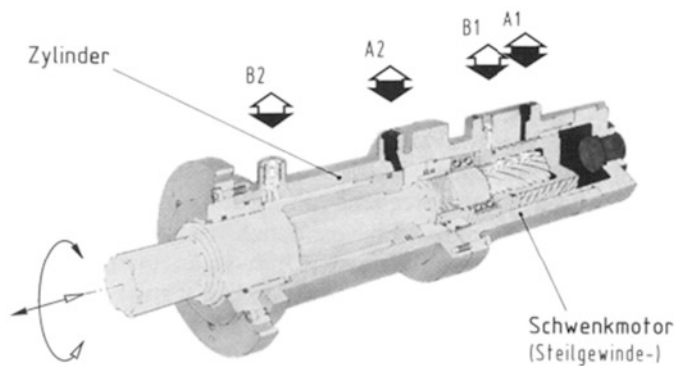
Steilgewinde-Dreh-Hubzylinder in der Gestaltungsvariante Zylinder vor Schwenkmotor (Langhubeinheit) mit Einzelansteuerung der Komponenten für Drehschiebung (DH, Hausherr)
